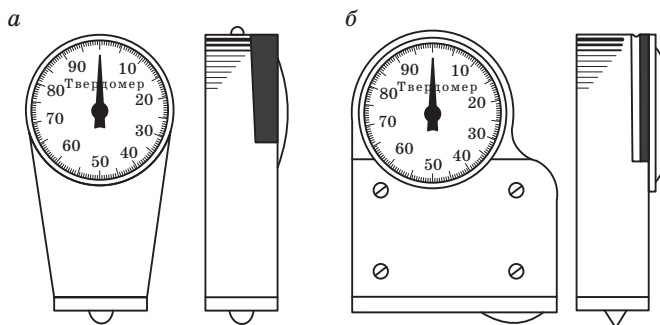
Твердомеры для определения поверхностной твердости литейных форм
